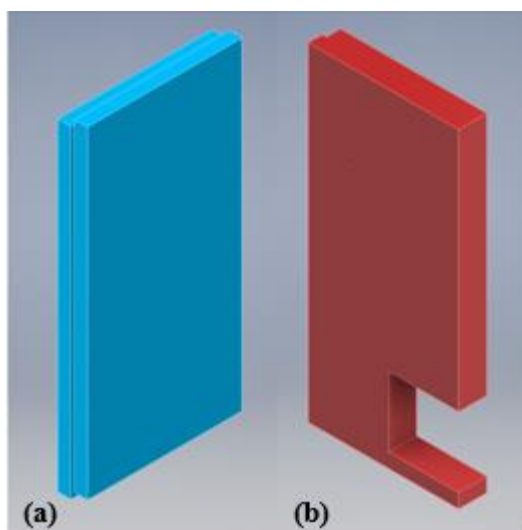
Modelação 3D das placas - (a) placa com a geometria inicial; (b) placa cortada
